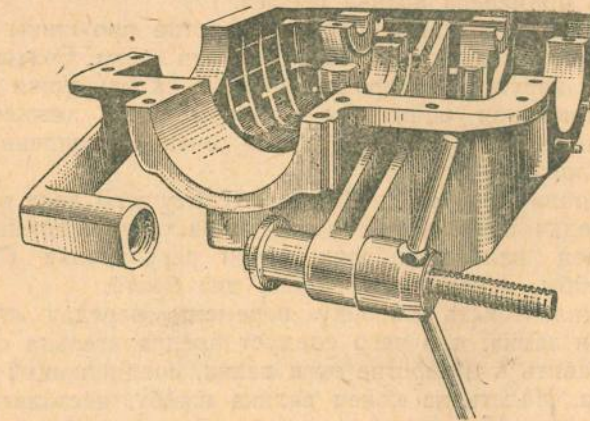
Запрессовка втулки в кронштейн картера коробки перемены передач
